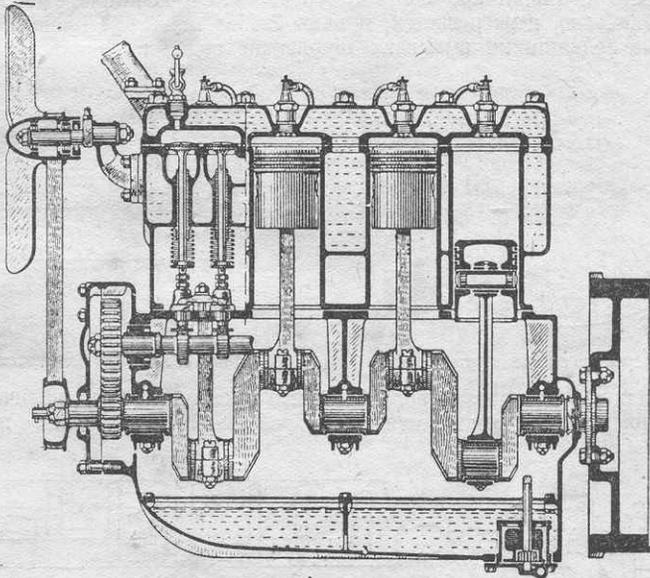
Продольный разрез четырехцилиндрового двигателя.
